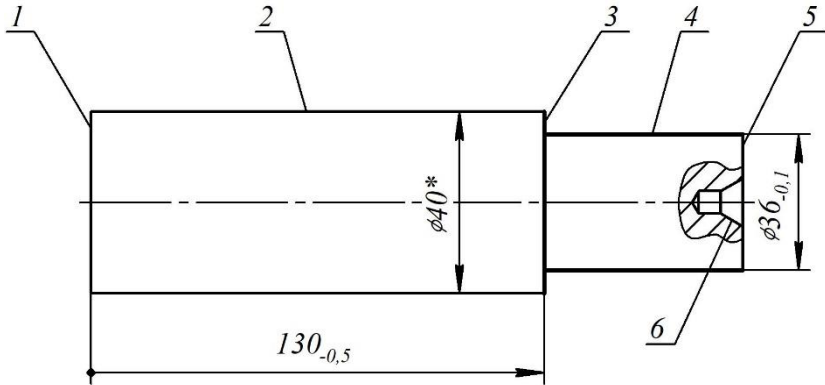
Схема базування вала в призмах з упором у торці (операція фрезерно-центрувальна)
